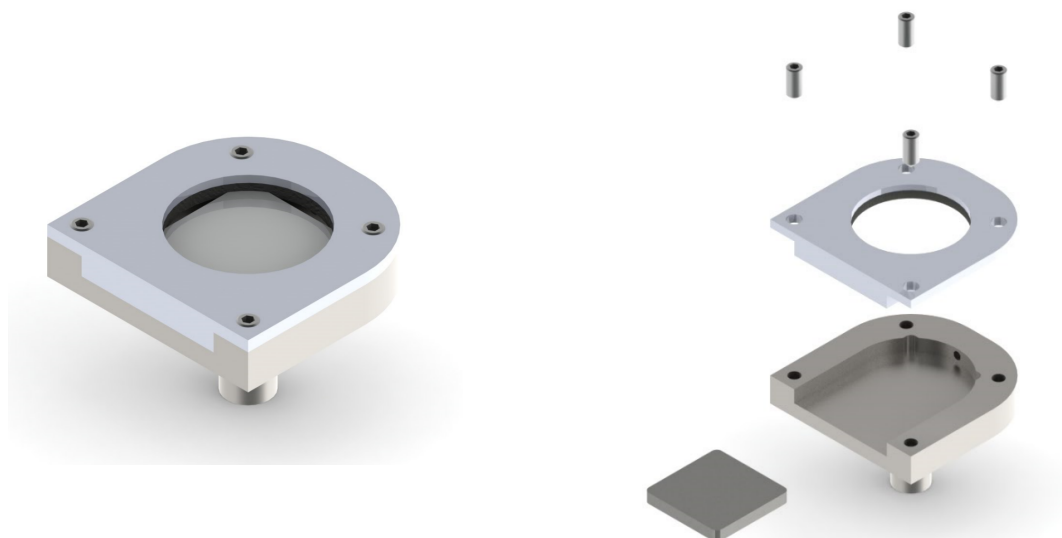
Sistema 4 - vista da montagem e vista explodida.
